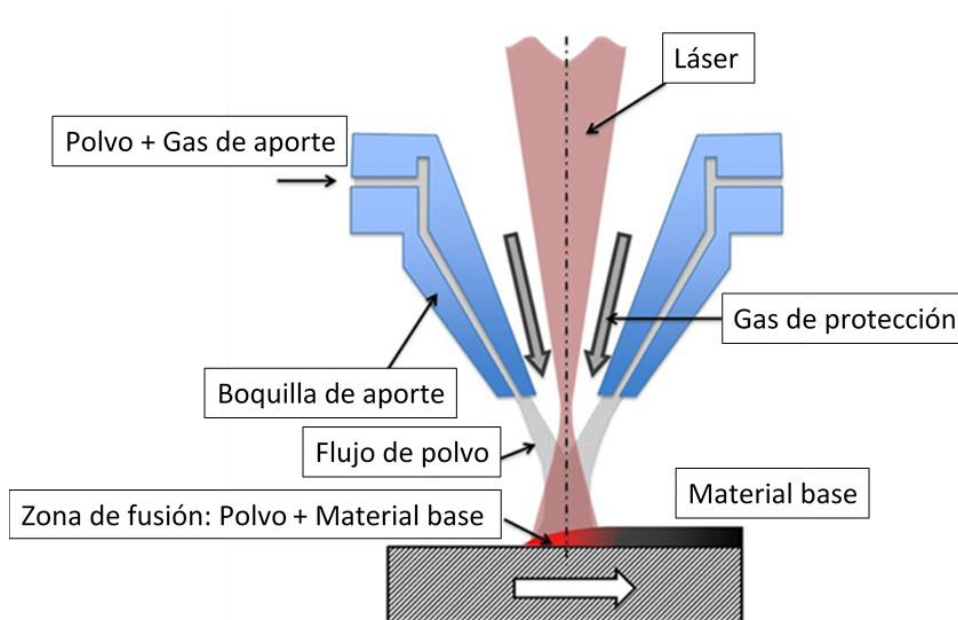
c Esquema de máquina de inyección directa de material.
